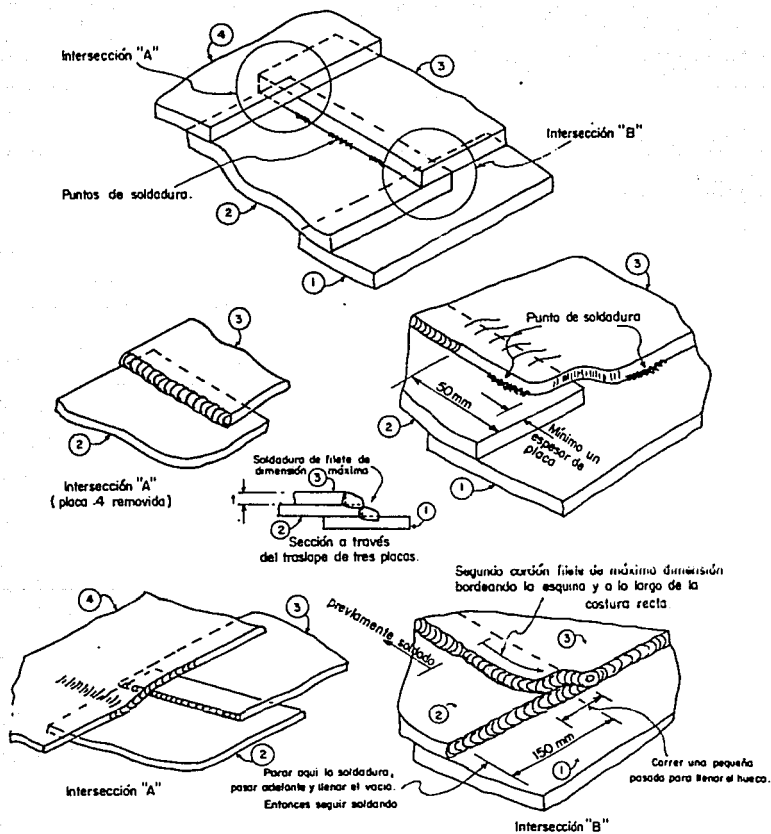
DETALLES DE SOLDADURA EN LA INTERSECCION DE LAS PLACAS
